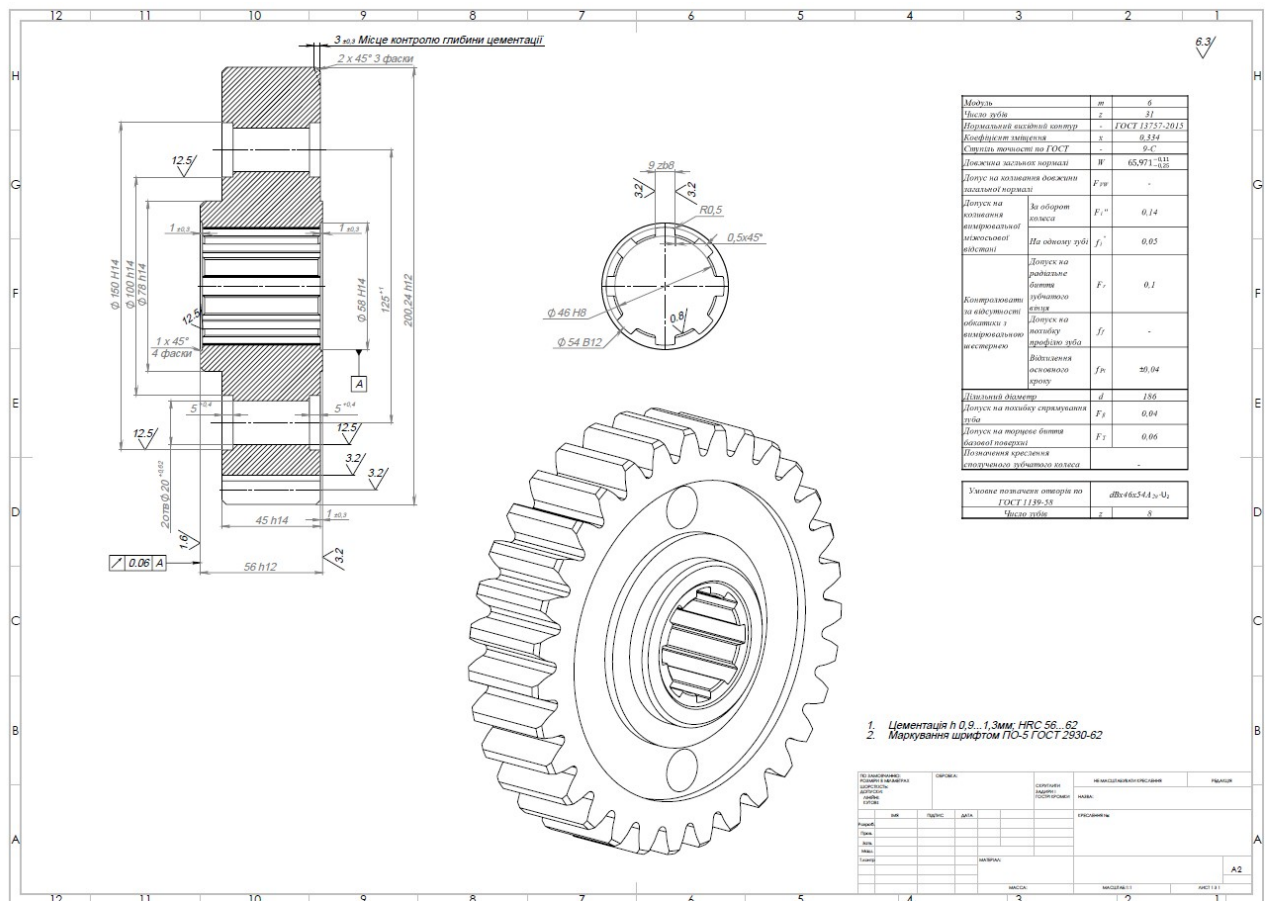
креслення зубчастого колеса БФКТБ 471.213
